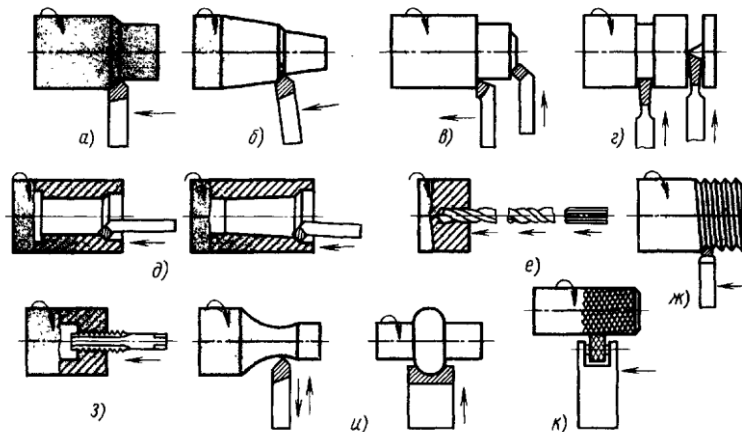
Основні види токарних робіт (а – обробка зовнішніх циліндричних поверхонь, б – обробка зовнішніх конічних поверхонь, в –
